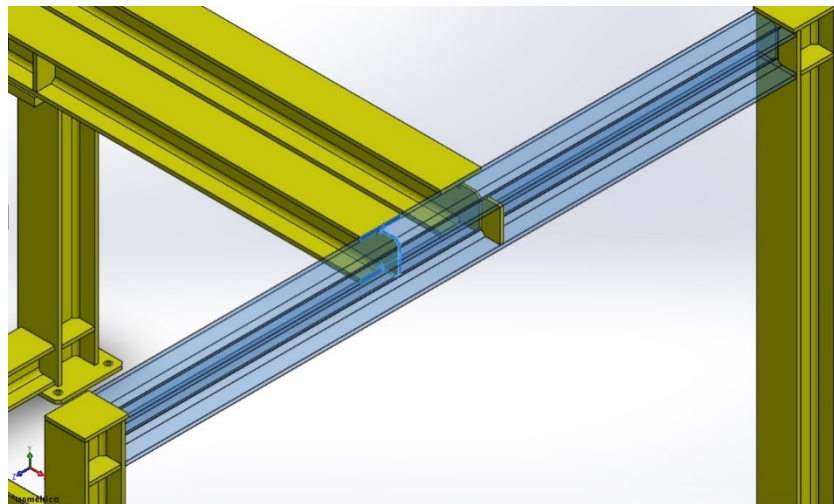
Detalle de las partes de la unión soldada crítica del aparato de carga
